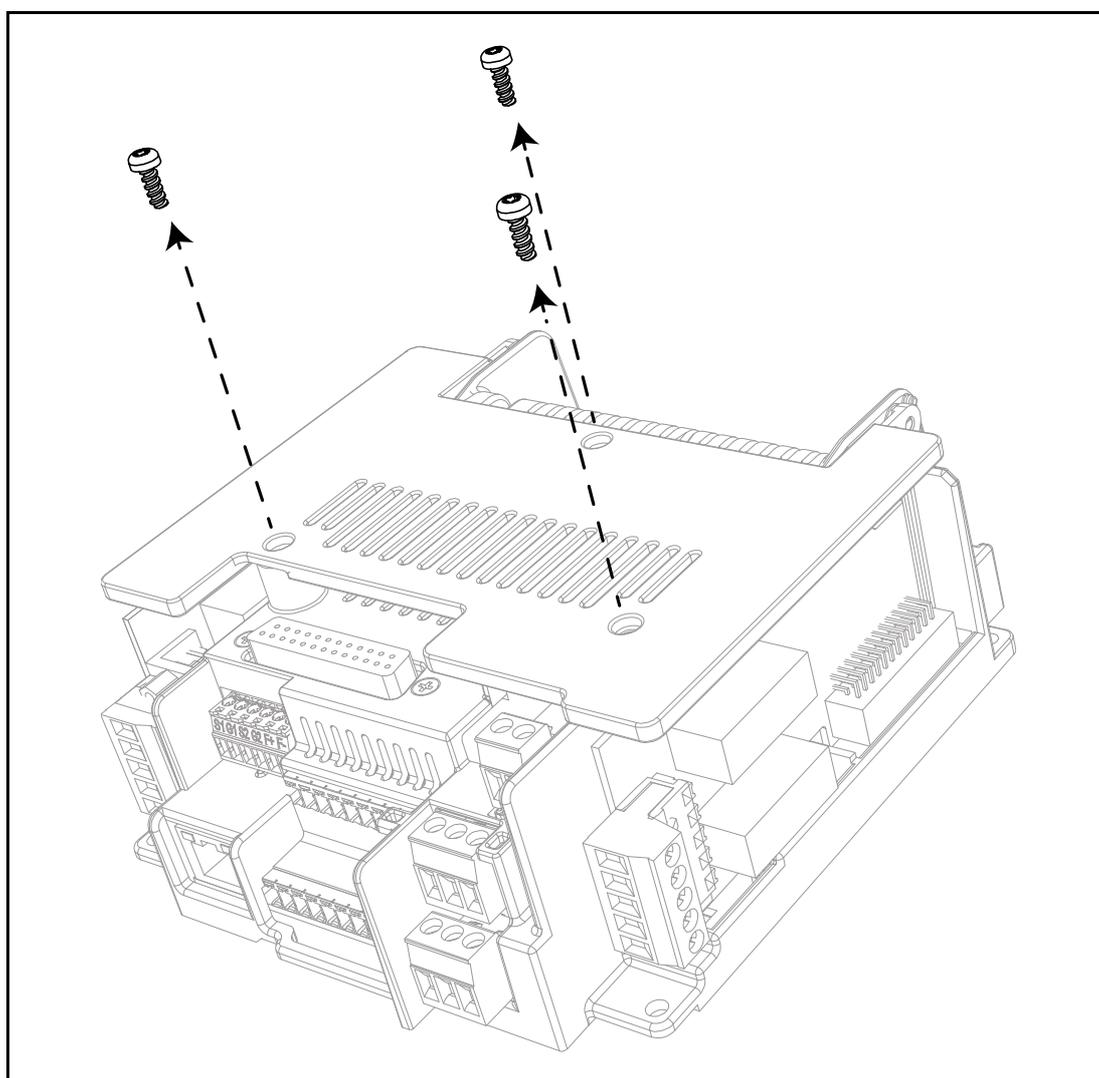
Entfernen Sie die drei Schrauben am Abdeckung.
